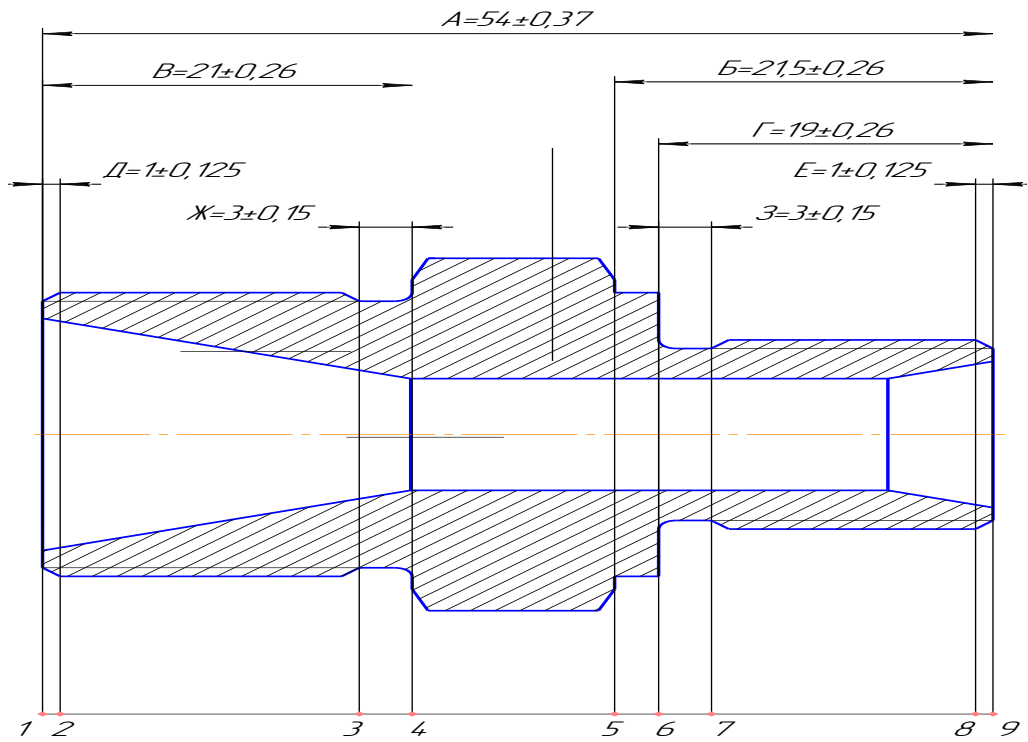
Преобразованный чертеж базовой детали на ось OX
